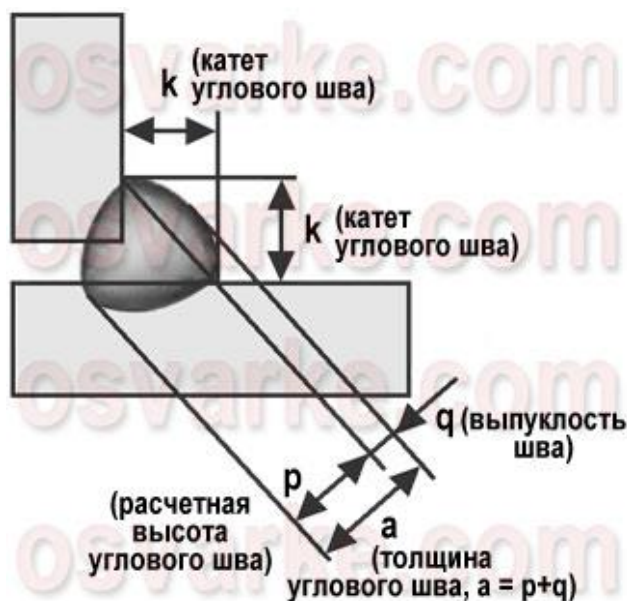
б. Геометрические параметры сварного шва.
